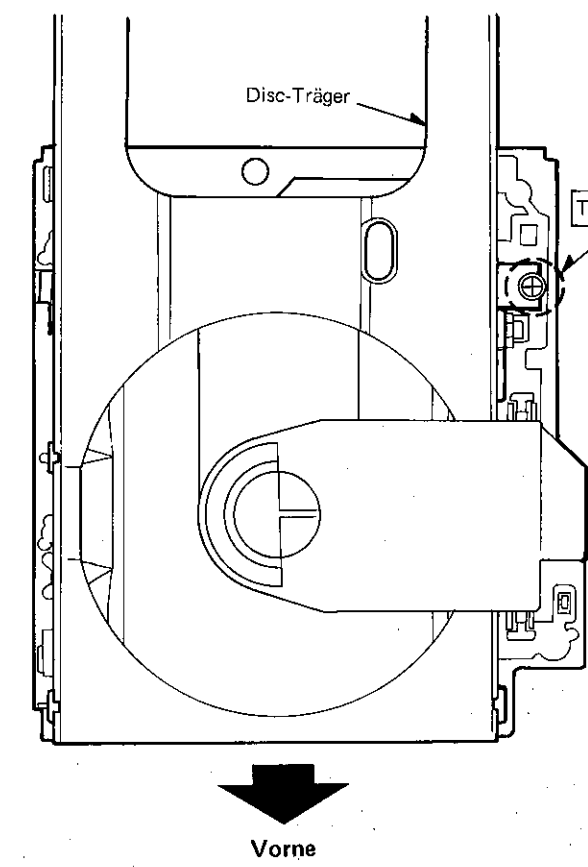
Abb. A : Mechanismus-Baugruppe (Draufsicht)
